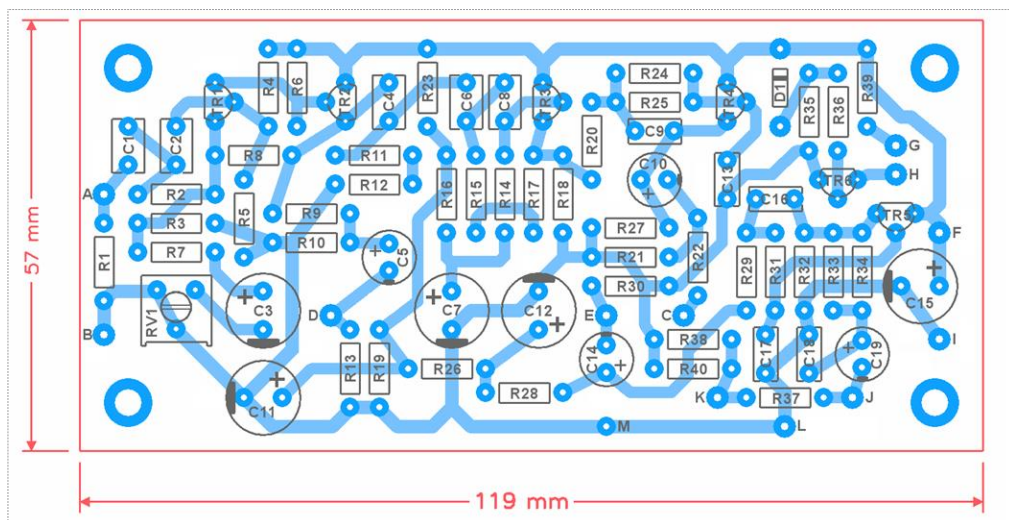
Placa de circuito impresso. Lado dos componentes.
